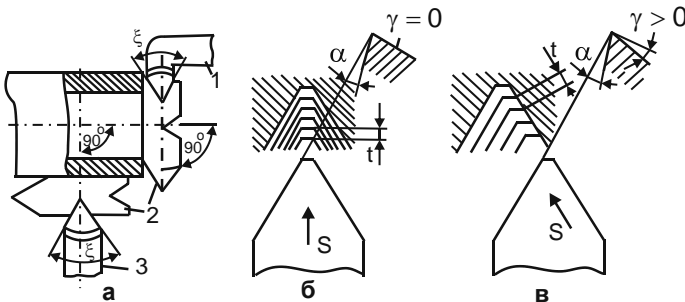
Схеми нарізання різьблення різцями на токарному верстаті
